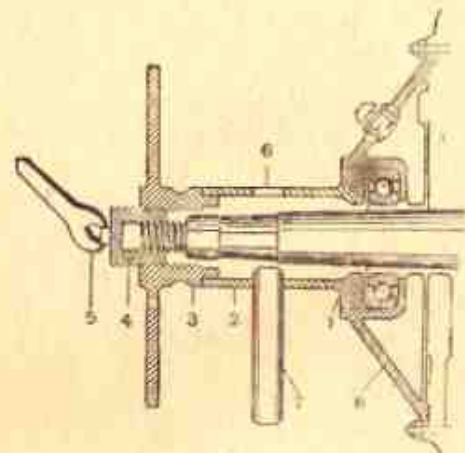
Приспособление для запрессовки коробки газораспределения на передний опорный шарикоподшипник.
